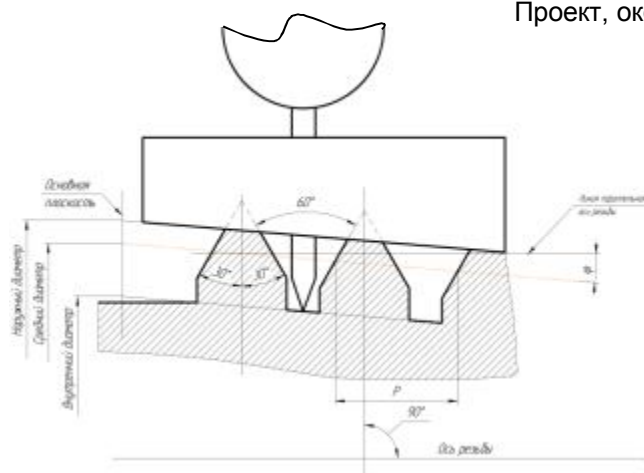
Измерение высоты замковой резьбы на трубе
